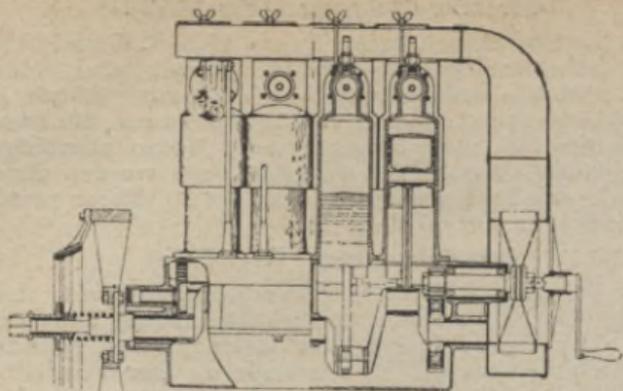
f. Luftgekühlter 20 PS Orient-Motor.
